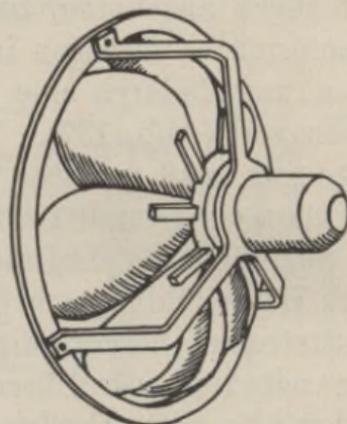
Schraubenlüfter mit muldenförmigen Schaufeln.
